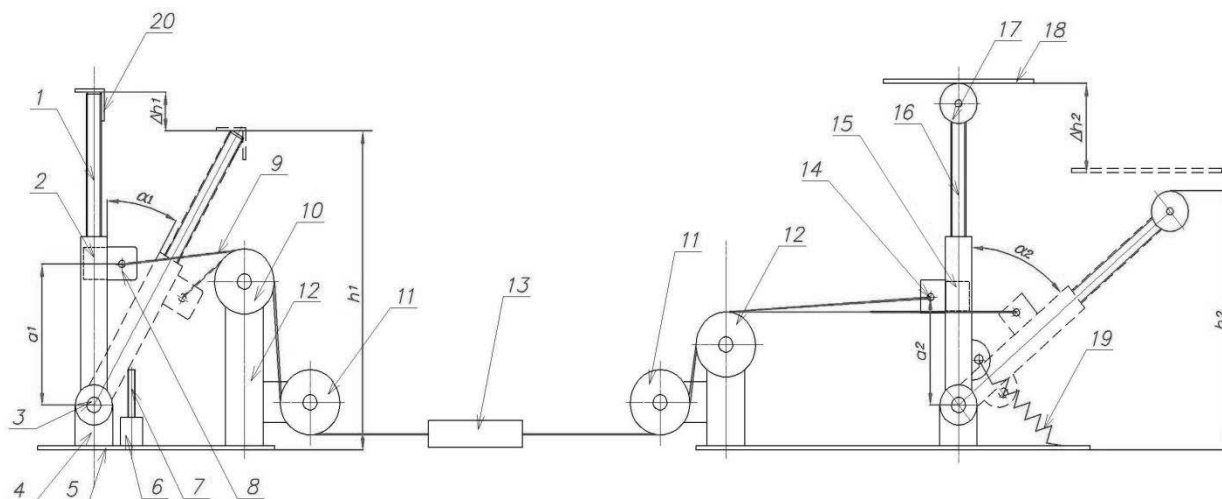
Схема устройства с регулируемой высотой подъема кузова для разгрузки ходовой части и шин пожарного автомобиля:
